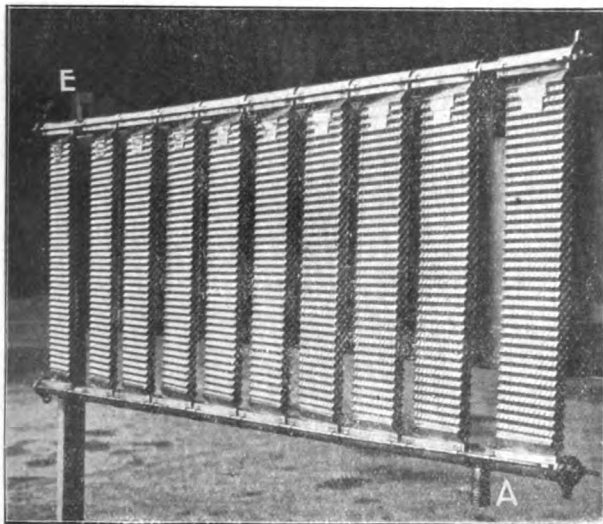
Kühler, fertig zusammengesetzt; E = Einlaß; A = Auslaß.
